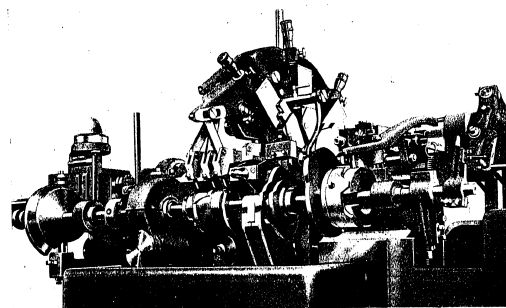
HINTERANSICHT DES HW-17 MIT DEN AUF DER STEUERWELLE BEFESTIGTEN KURVENSCHLEIFEN UND STEUERHEBELN
